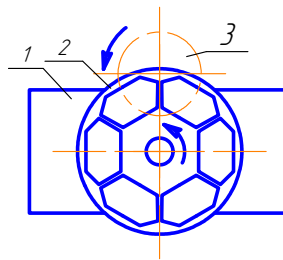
Схема работы барабанно-фрезерного станка: 1 – станина станка; 2 – вращающийся стол; 3 – торцовая фреза.
